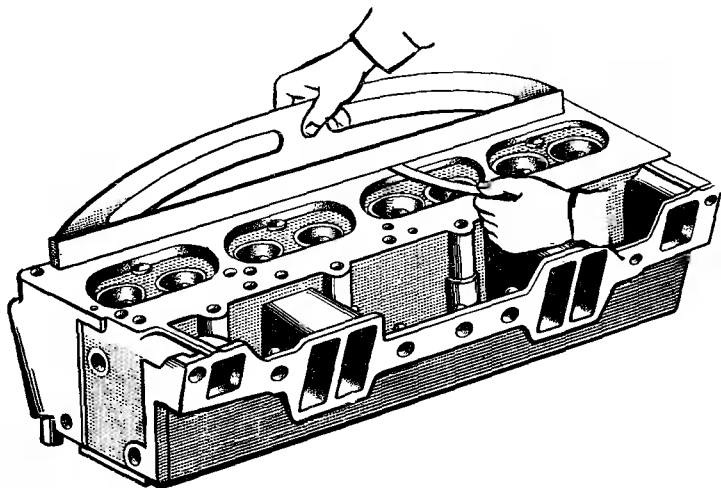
Контроль плоскостности привалочных поверхностей головки блока цилиндров линейкой и щупом
